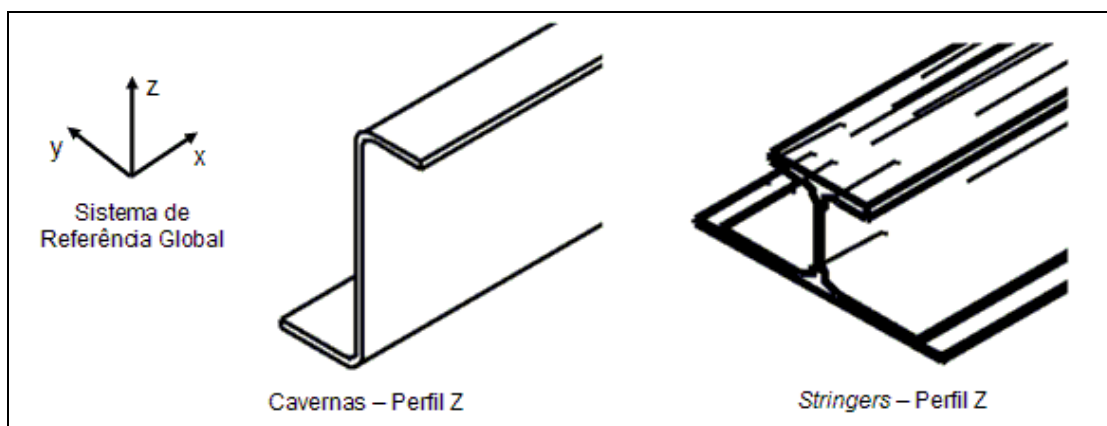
Detalhes dos perfis das vigas de reforço.
